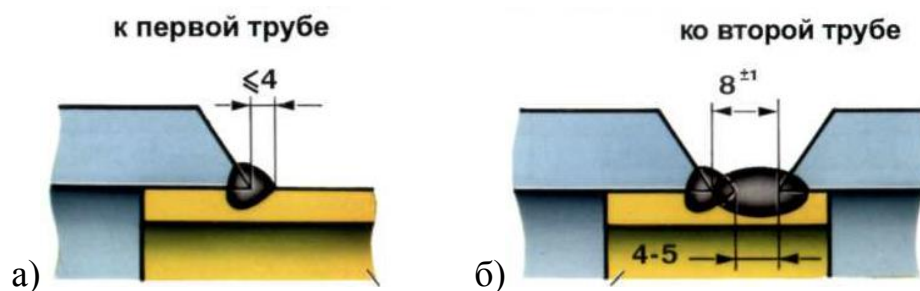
Особенности выполнения сварных швов при приварке подкладного кольца
